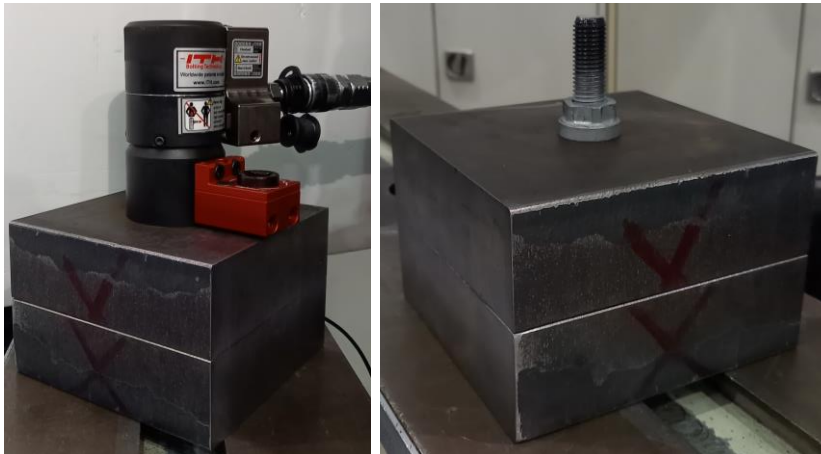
Hydraulisches Vorspannen der HV-Schrauben M16x160 mit Werkzeug der Firma ITH Schraubtechnik (links), montierte Schraubenverbindung mit spezieller Zugmutter (rechts)
